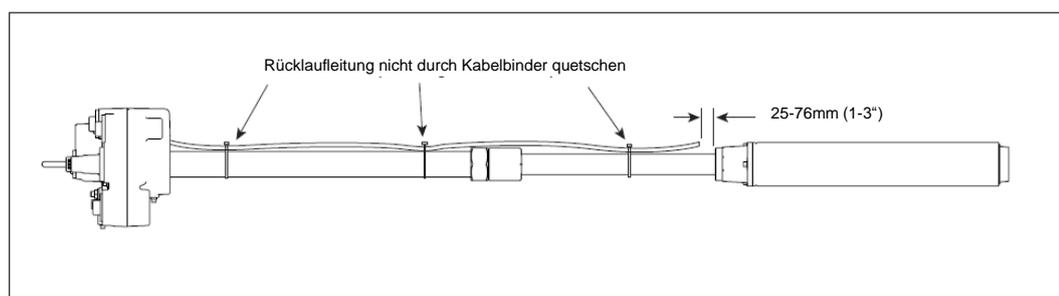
Die Befestigung des Kraftstoffrücklaufs
